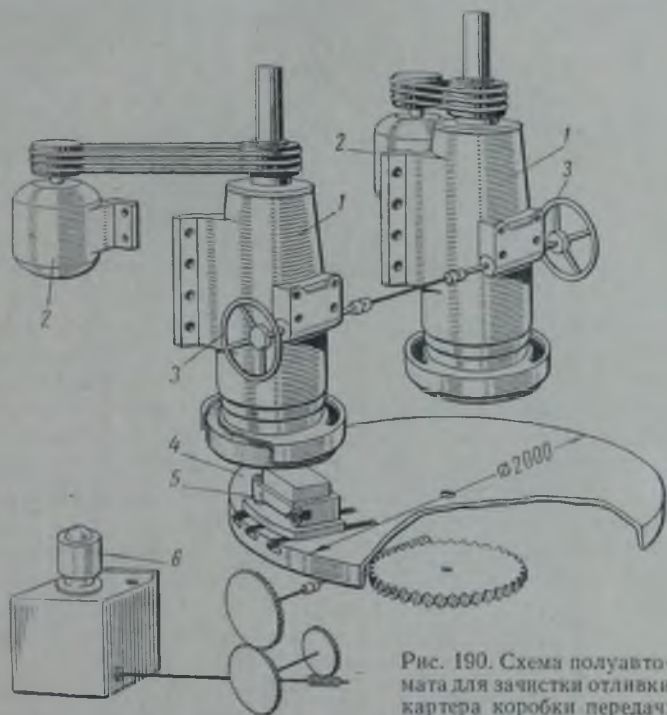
Схема полуавтомата для зачистки отливки картера коробки передач:
